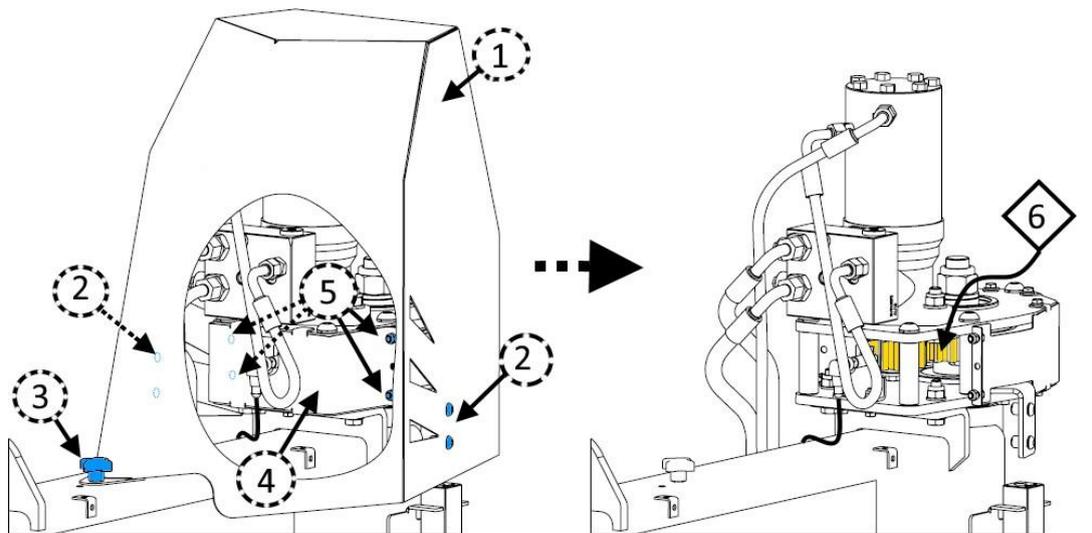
Engranaje de brazo de encintado: retirada de tapas y engrase.
